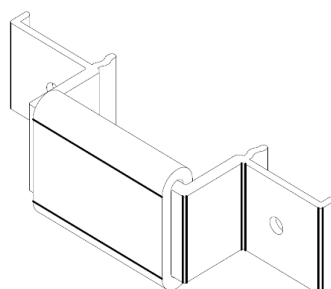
Pieza de cuelgue STB (ref. 05.19.130)
